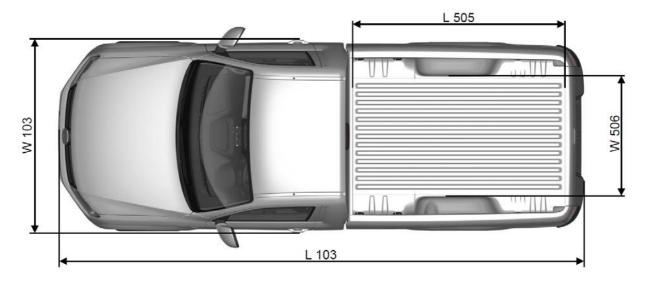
Vista en planta del Amarok SC (Single Cab)
